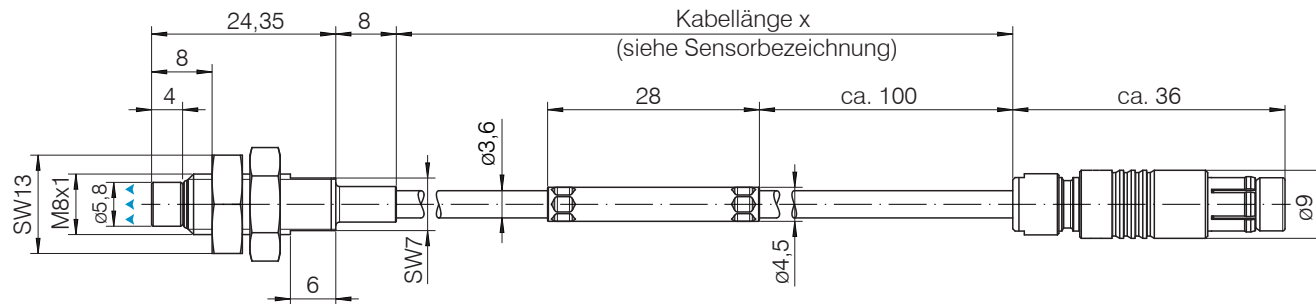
Maßzeichnung Sensoren ES-U2-C-CAx/mB0, Abmessung in mm
